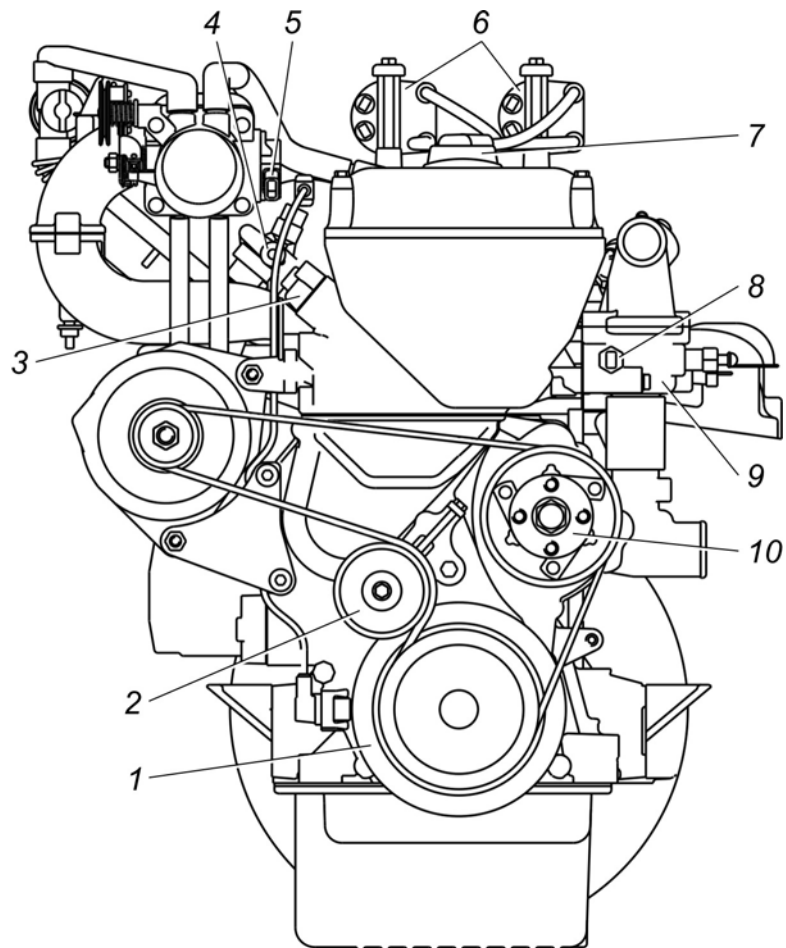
Вид двигателя спереди: 1 - шкив-демпфер коленчатого вала; 2 - натяжной ролик ремня привода агрегатов; 3 - крышка верхнего гидронатяжителя; 4 - топливопровод с форсунками; 5 - датчик положения дроссельной заслонки; 6 - катушки зажигания; 7 - крышка маслоналивного патрубка; 8 - датчик температурного состояния двигателя; 9 - корпус термостата; 10 - насос водяной с электромагнитной муфтой (НВЭМ)
